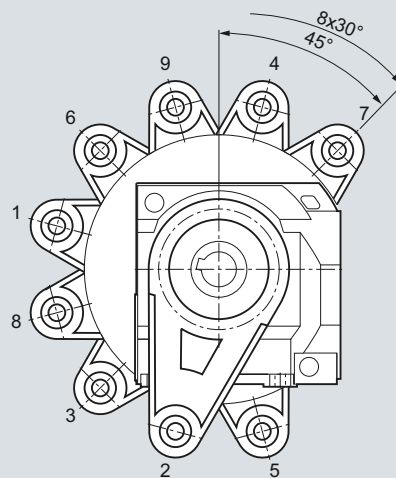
Stirnrad-schneckengetriebe C in Aufsteckausführung
